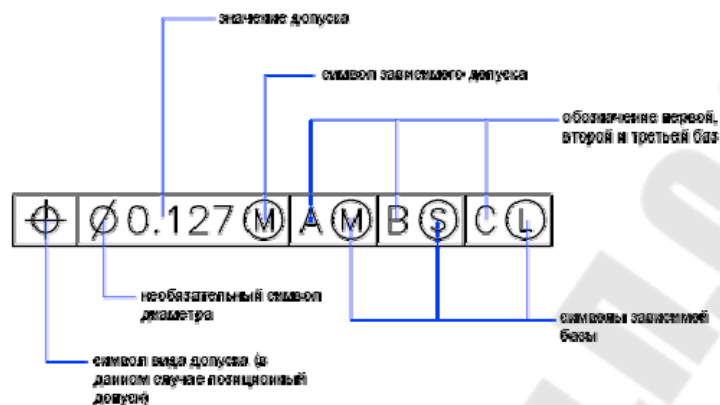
Обозначение допуска формы и расположения поверхностей
